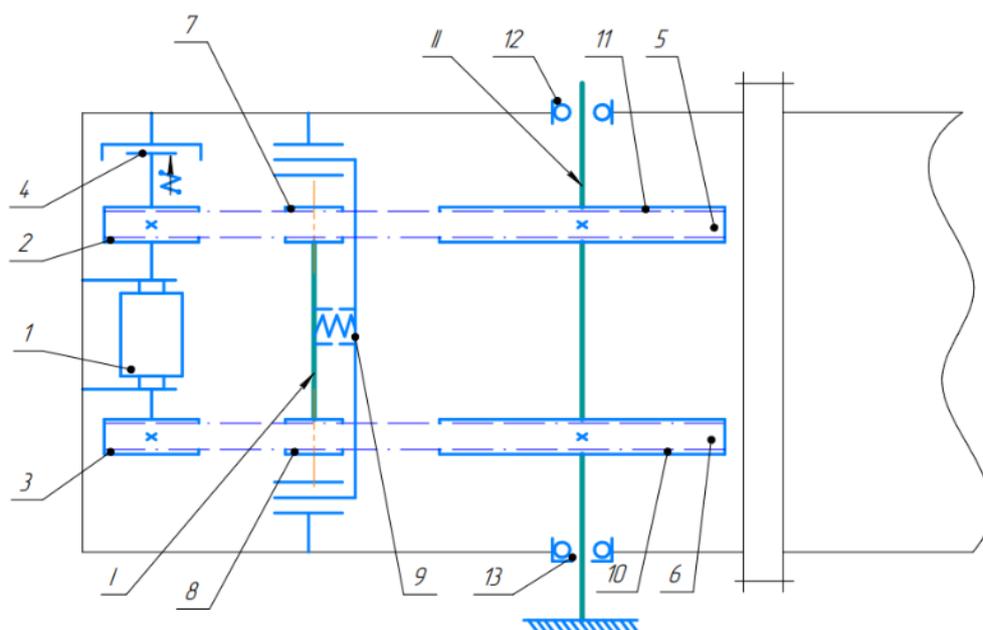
Привод поворотный принципиальная кинематическая схема вариант с цепной передачей.
